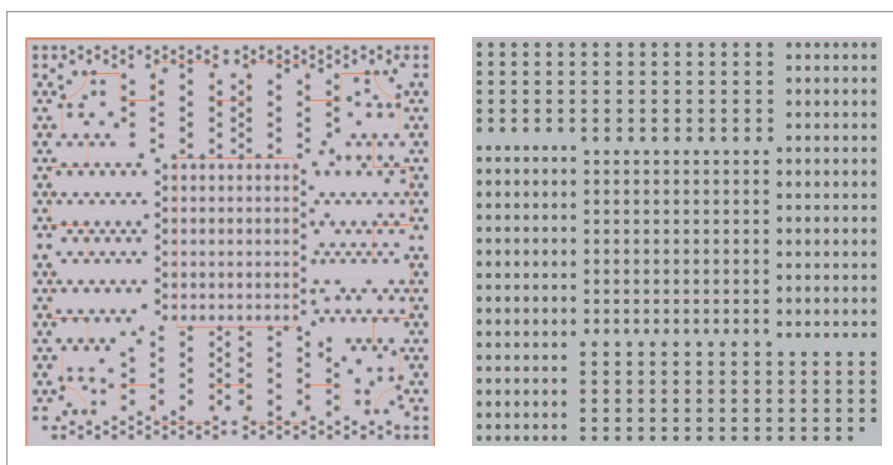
Частично регулярное расположение контактов корпуса BGA
